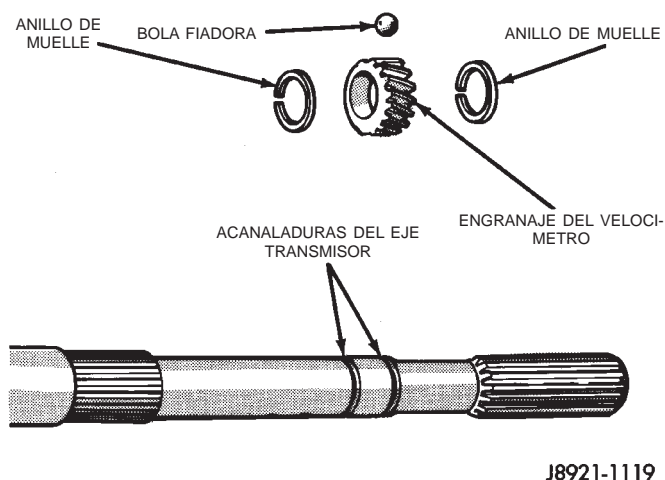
Ensamblaje del engranaje propulsor del velocímetro
